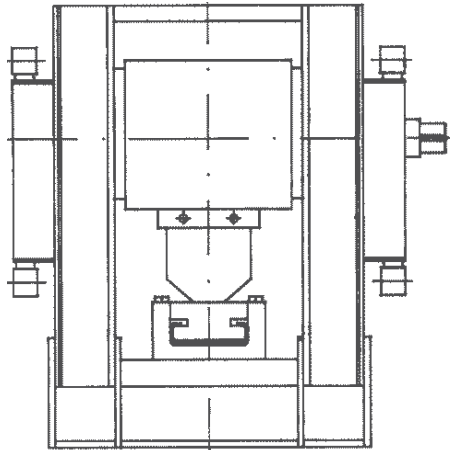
Ножницы, вид по направлению движения разрезаемой полосы
